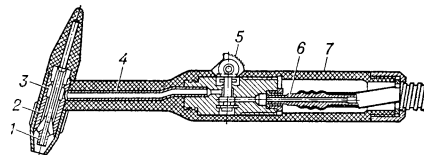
Ручная горелка для сварки неплавящимся электродом: 1 — токоподводящая цапга; 2 — сопло; 3 — газовая камера; 4 — мундштук; 5 — газовый вентиль; 6 — газовый канал и токопровод; 7 — рукоятка.
